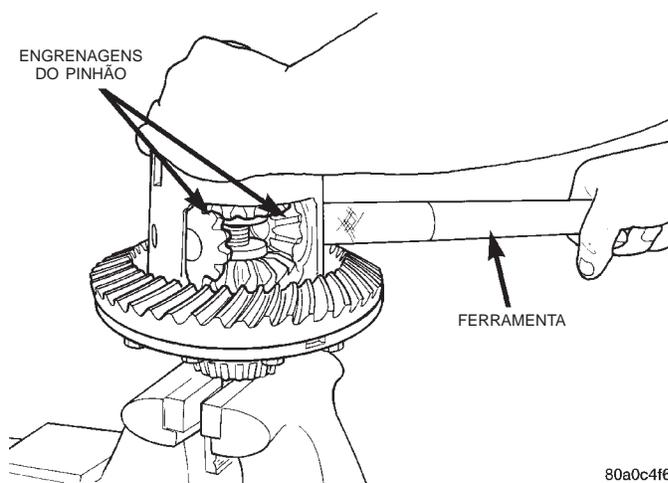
Remoção da Arruela de Escora da Engrenagem do Pinhão
